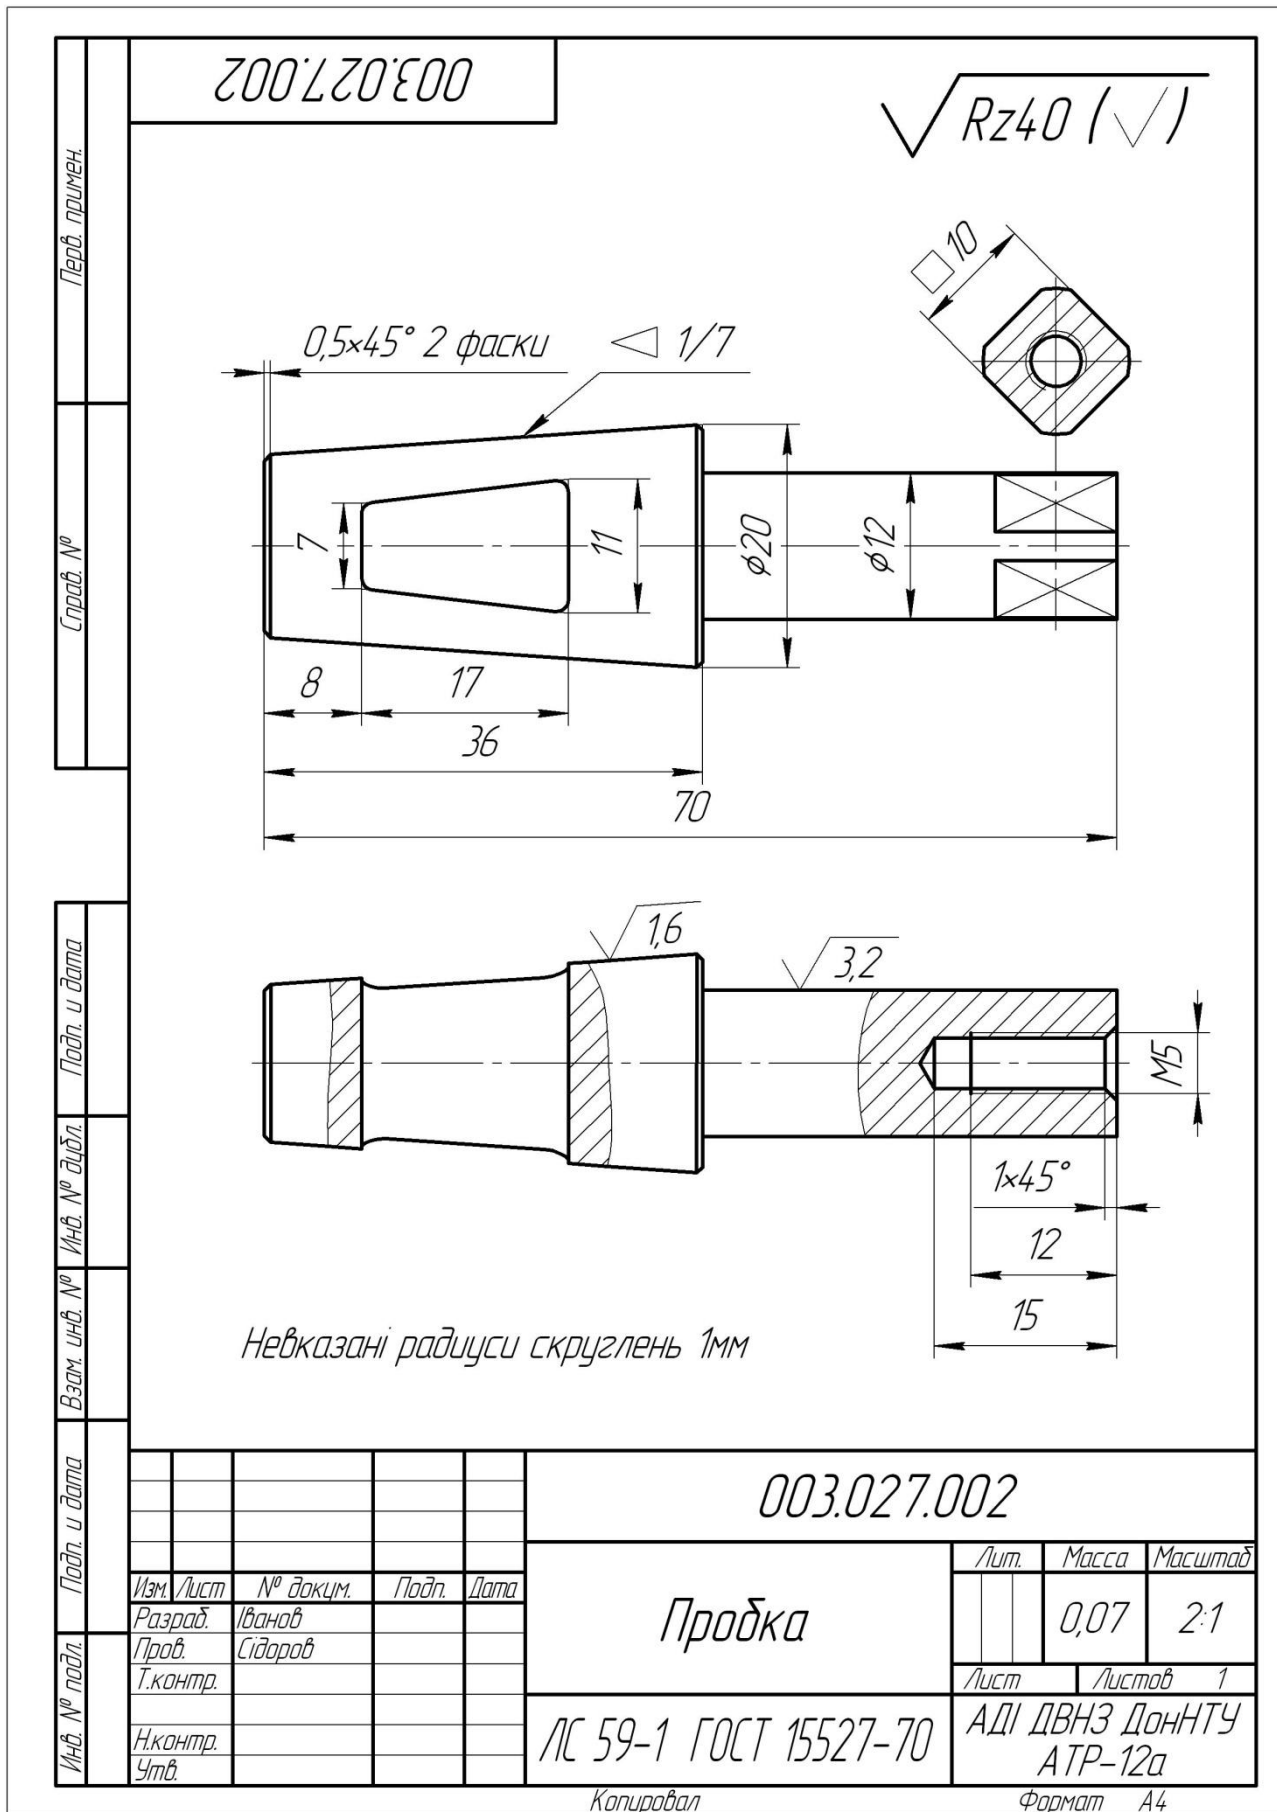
Приклад робочого креслення деталі «Пробка»
